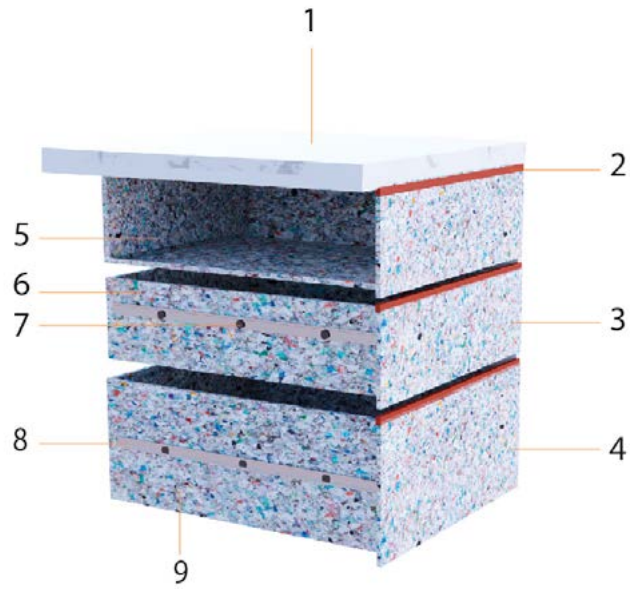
Detalle constructivo 3d cajonera HDPE reciclado
